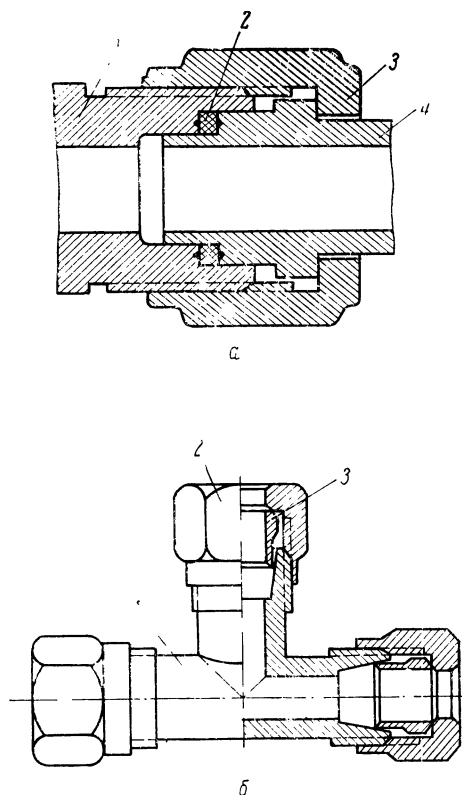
Соединения фреоновых трубопроводов: а — штуцерно-торцевое; 1 — штуцер; 2 — прокладка; 3 — накидная гайка; 4 — ниппель; б — с уплотнительным металлическим кольцом; 1 — корпус; 2 — накидная гайка; 3 — уплотнительное кольцо.
